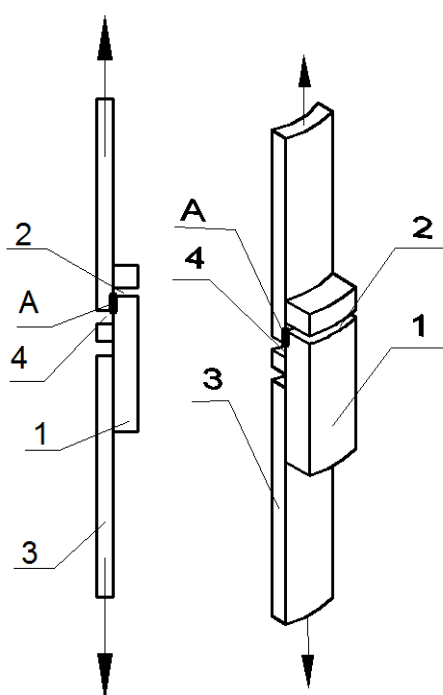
Образец для определения прочности раструбной сварки
